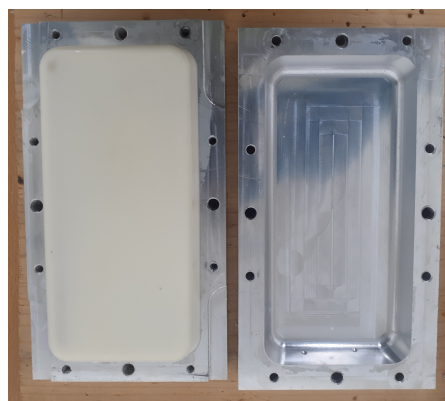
Molde maquinado em alumínio após rotomoldagem
